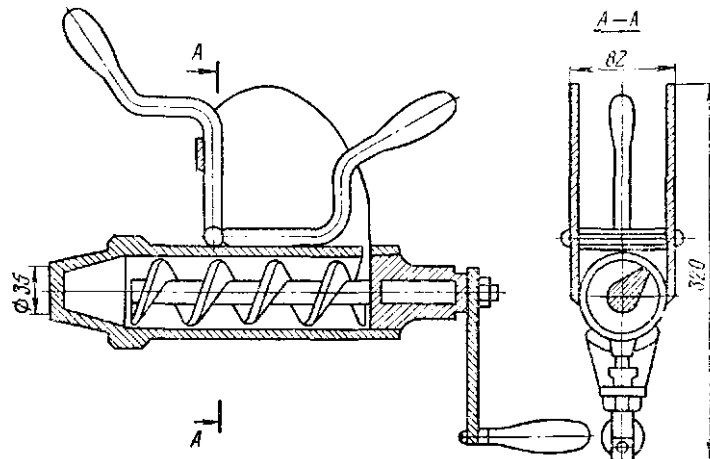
Приспособление ПР-1 для изготовления пыжей из пластичных материалов
